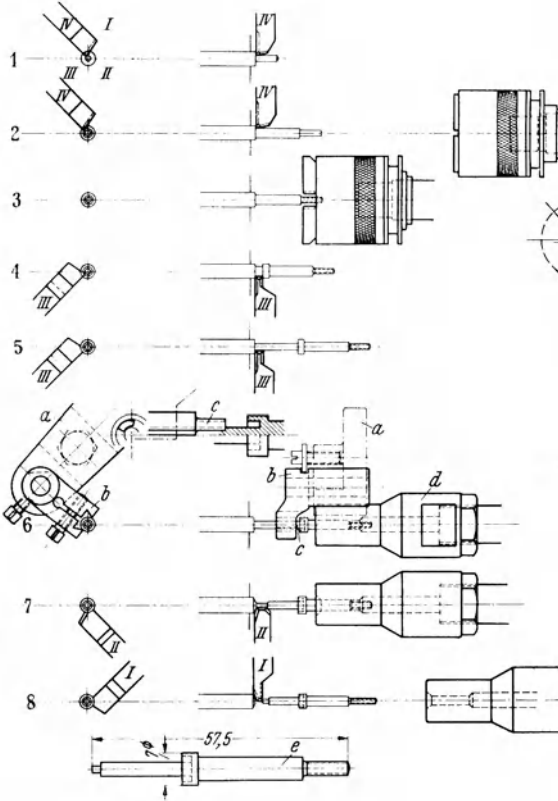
Bearbeitung eines Messingstiftes (e).
